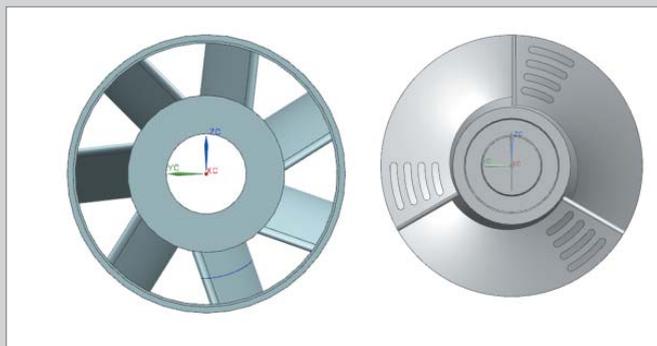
Общий вид осевой ступени – направляющий аппарат и рабочее колесо
